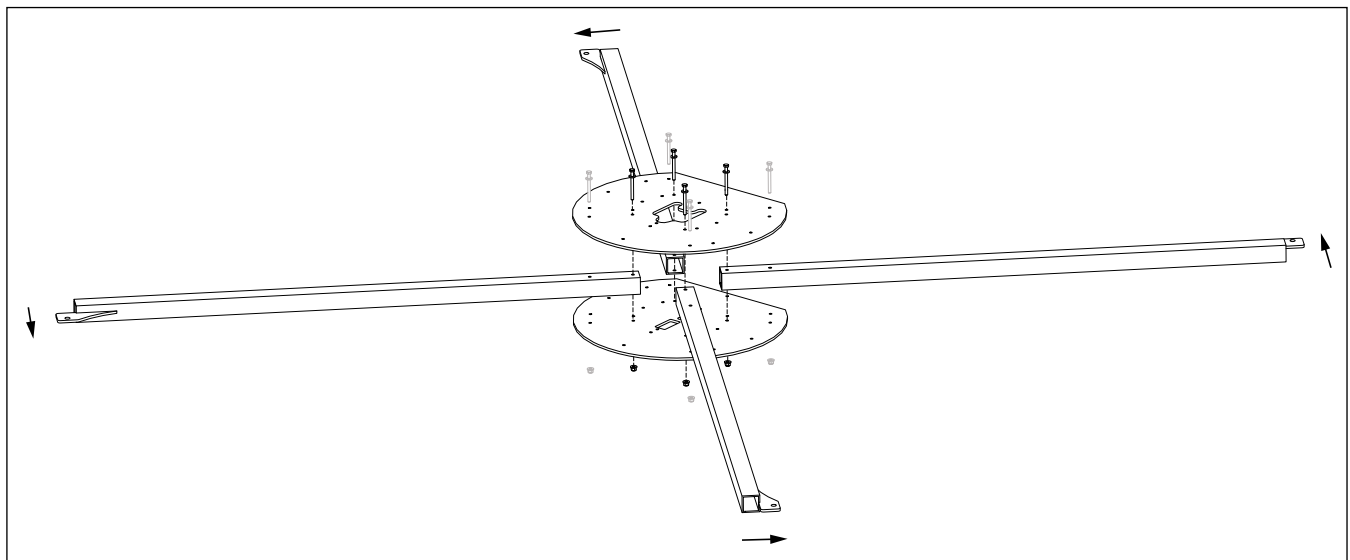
Ausrichtung der Montagearme am Sensor-Array
